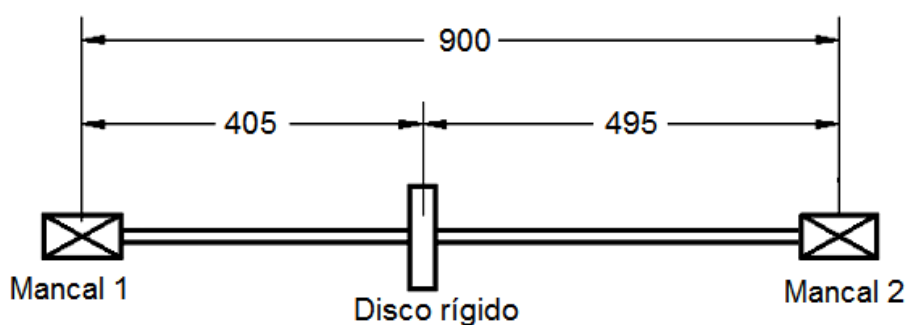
Desenho esquemático do rotor com disco massivo em posição assimétrica
